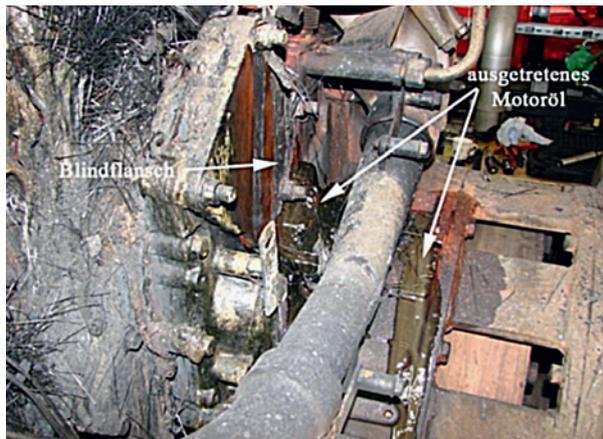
Kompressorblindflansch an der zum Generator gerichteten Seite des Motors. Der extreme Ölaustritt nach nur wenigen Motorumdrehungen ist offensichtlich
